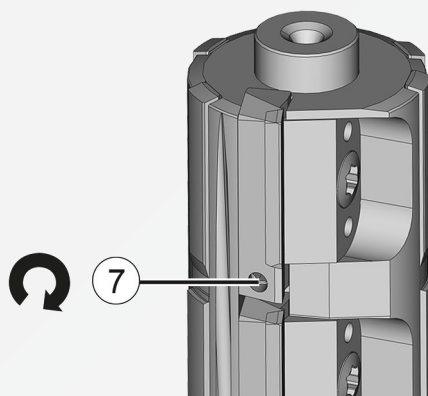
Réglage de l'arête de coupe de l'outil sur la fin de course axiale
